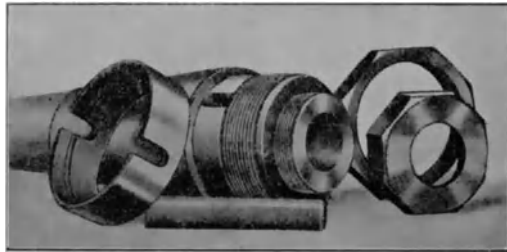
d. Die einzelnen Teile der Fräsdornbefestigung.
